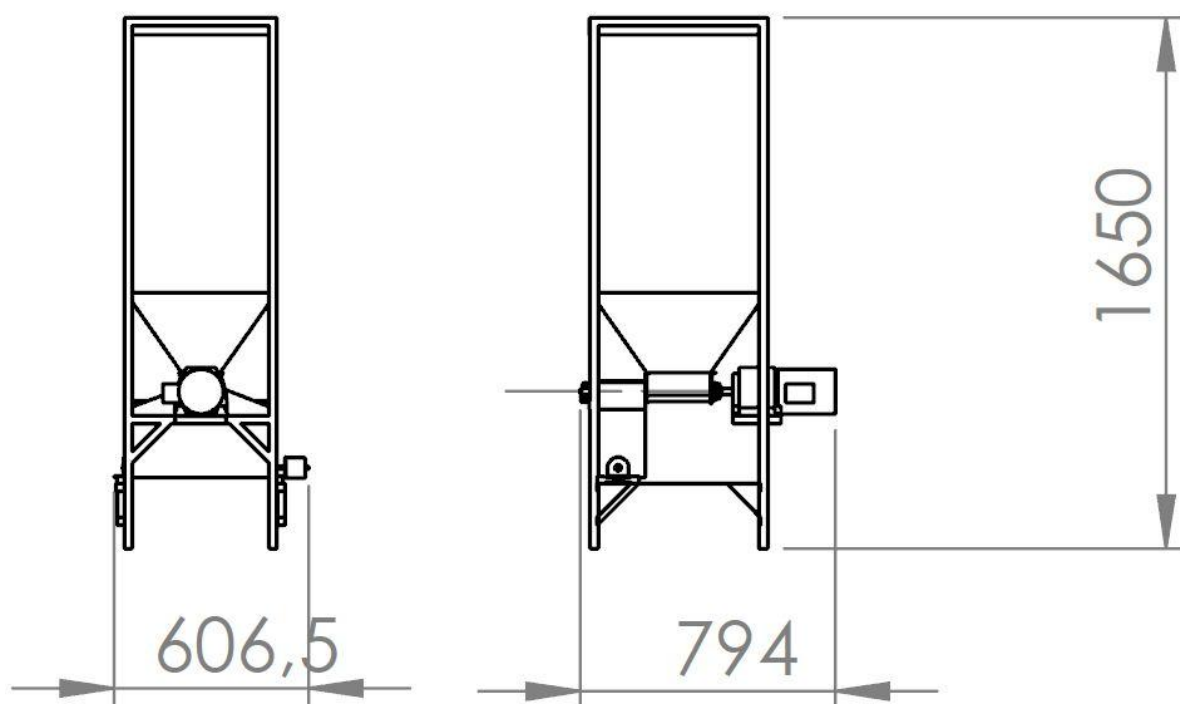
Vista lateral e frontal do protótipo (cotas em milímetros)
